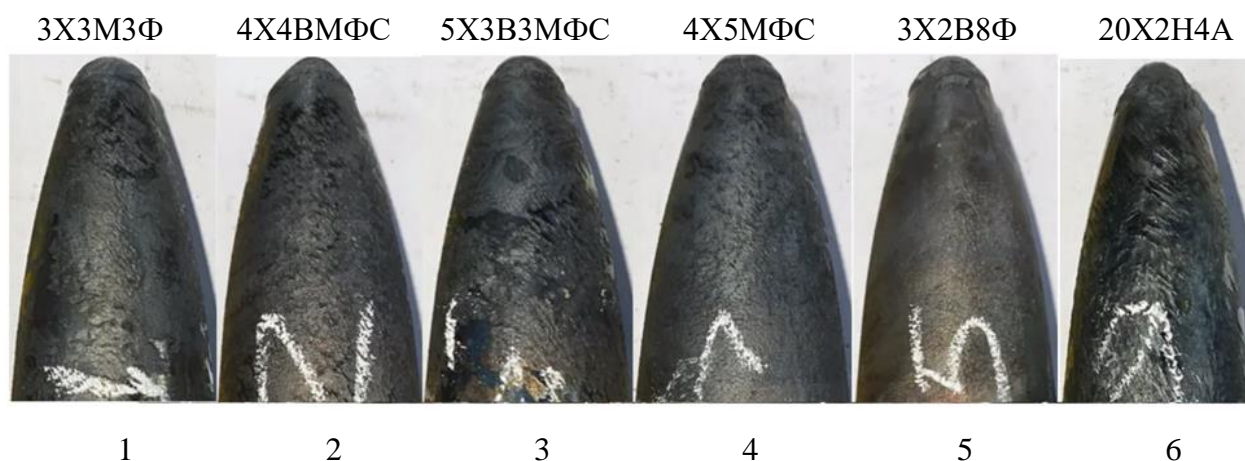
Состояние рабочей поверхности и носка оправок после прошивки пятой заготовки.
